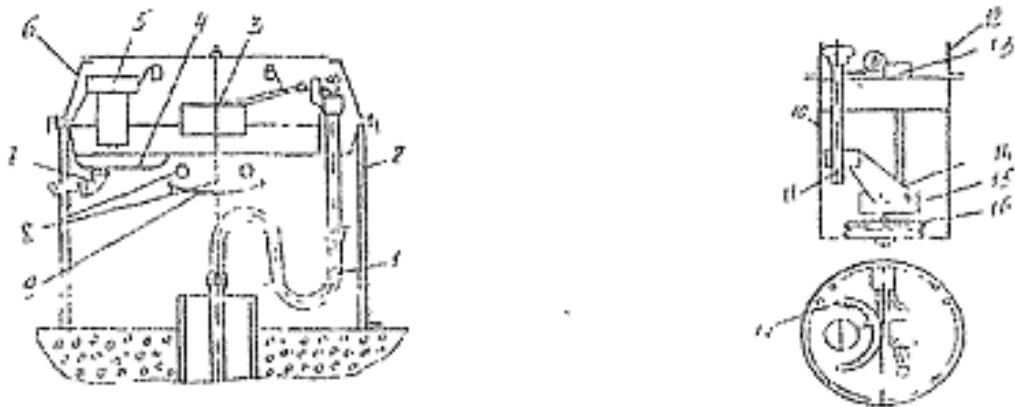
Автонапувалка АГК-4: а - схема автонапування: 1 - гумовий рукав; 2 - теплоізоляція; 3 - клапанно-поплачковий механізм; 4 - чаша; 5 - терморегулятор; 6 - кронштейн; 7 – зливальна труба; 8 - нагрівальний елемент; 9 - відбійник; б - терморегулятор; 10 - склянка; 11 - регулювальний гвинт; 12 - кришка; 13 - перехідна колодка; 14 - кронштейн; 15 - мікроперемикач; 16 - мембрана; 17 – шкала
